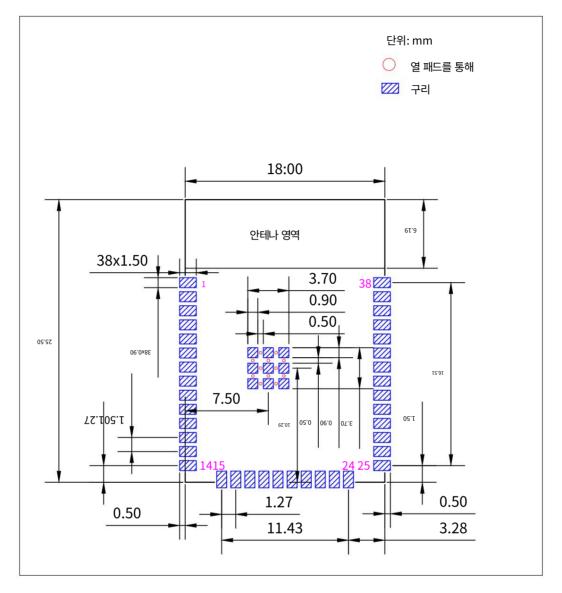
ESP32WROOM32D의 권장 PCB 랜드 패턴
